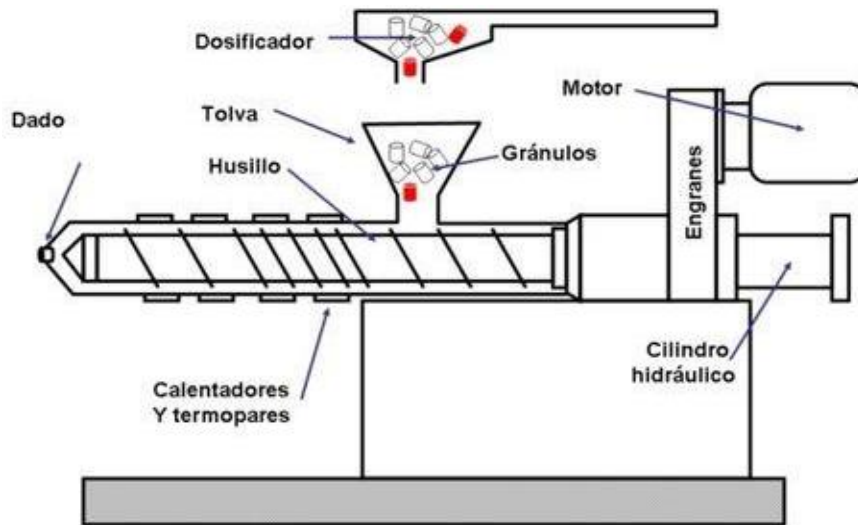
Diseño genérico de una máquina extrusora (Benavente, 2011)
